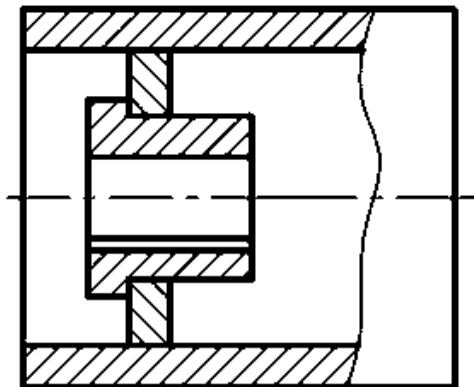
Образец выполнения чертежа сварного соединения.
